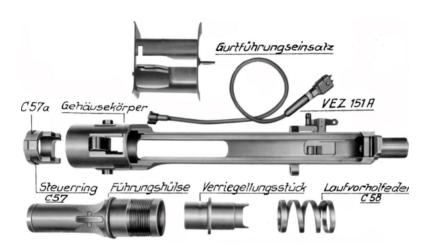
Gehäuse: Hauptteile (Ansicht von oben)
